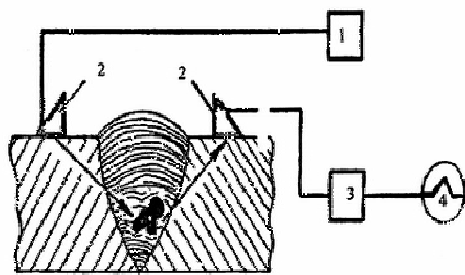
Принципиальная схема установки для обнаружения дефектов сварных швов.
